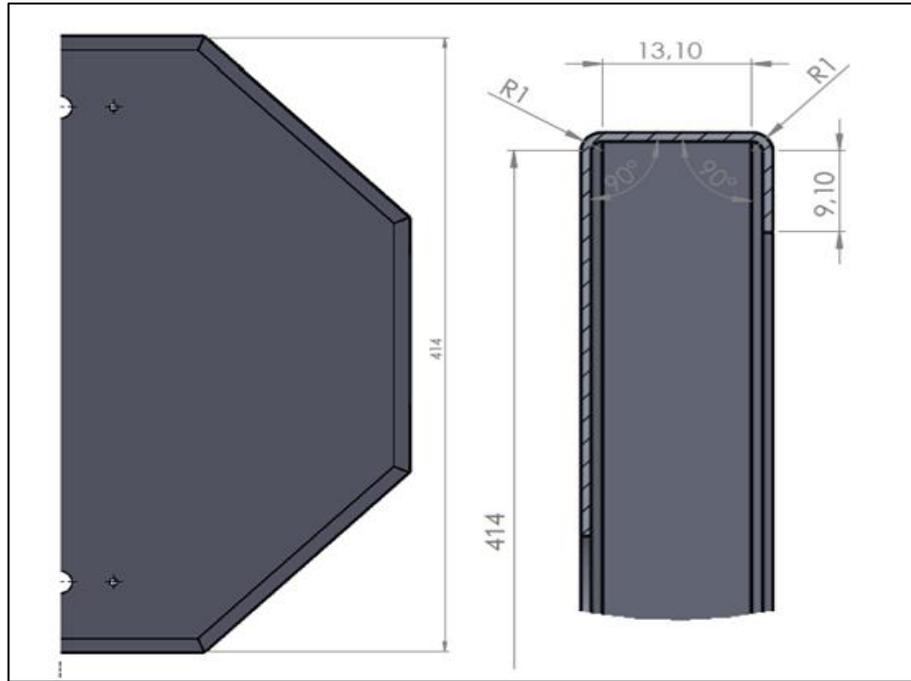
Dimensiones en vista detallada del Rótulo “Disco Pare”.
